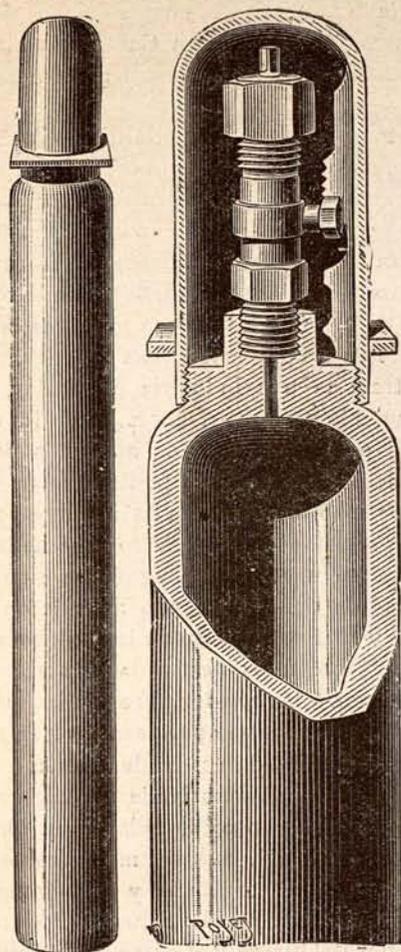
Bombona sin soldadura para gases licuados.
